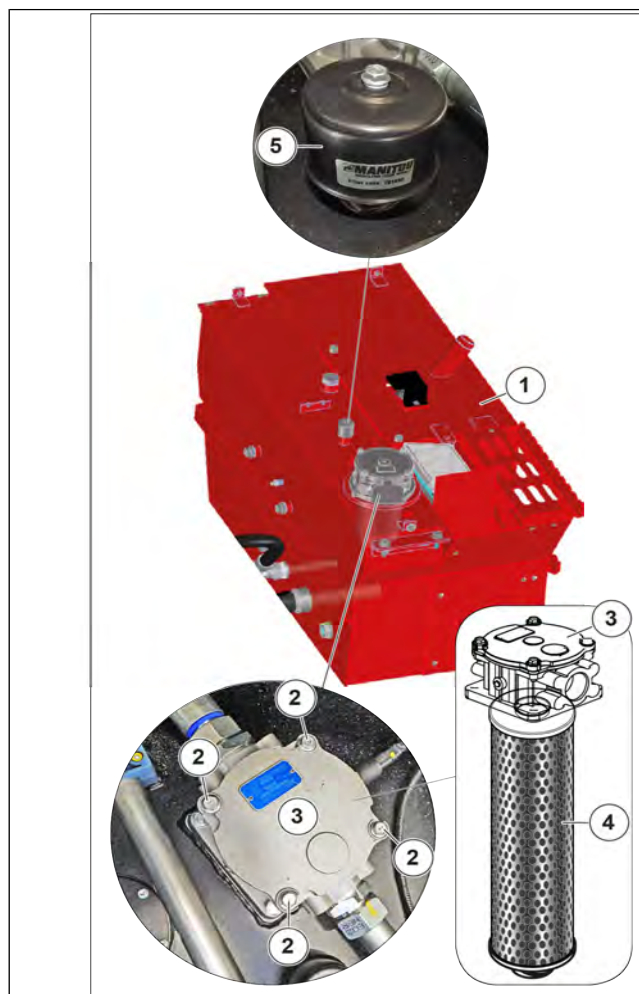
Remplacement de la cartouche du filtre à huile hydraulique (vidange)
